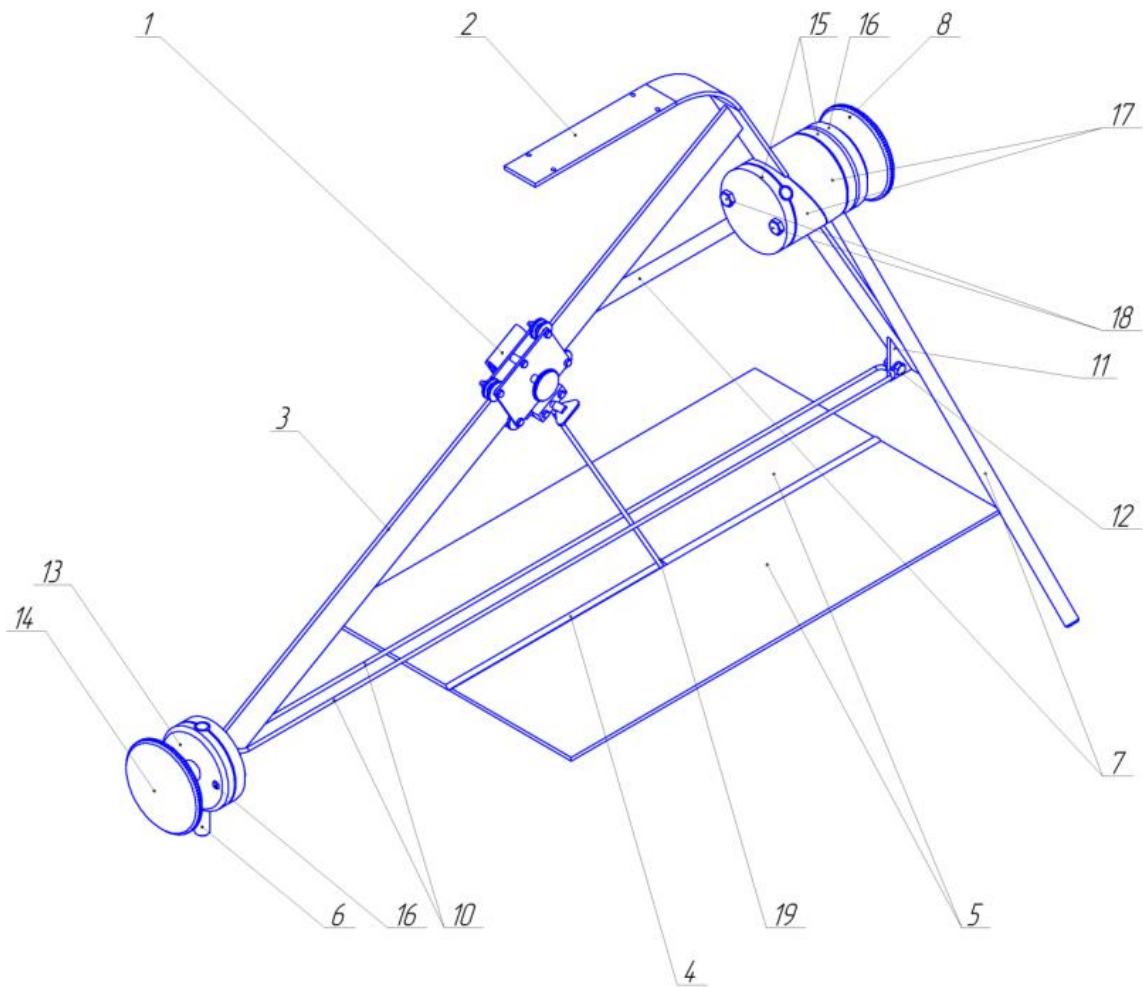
Конструкція установки для гравітаційного зварювання
